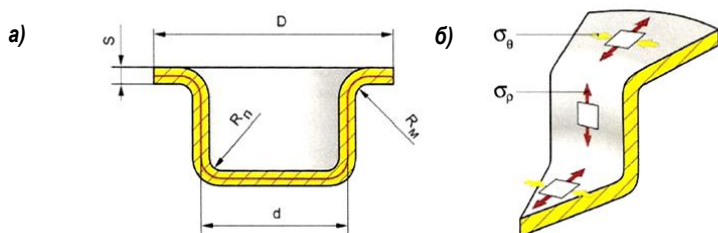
Обозначение размеров заготовок и напряжения, действующих в них
